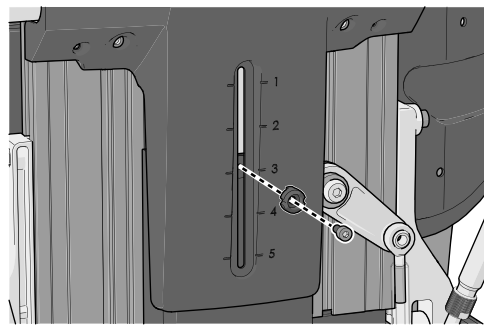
Der Kunststoffknopf ist mit einer Schraube befestigt.
